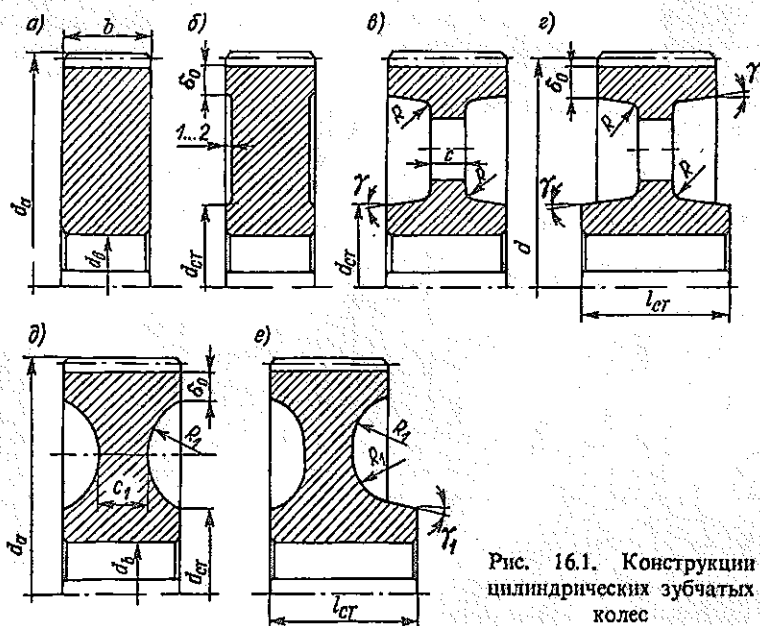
Конструкции цилиндрических зубчатых колес
